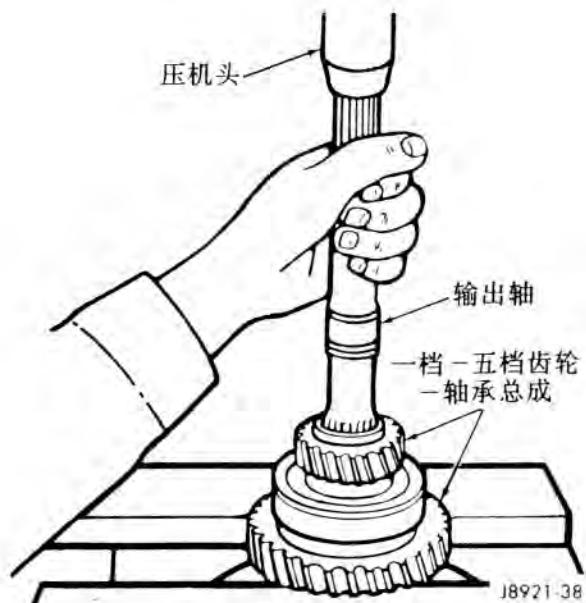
拆卸五档齿轮、一档齿轮、后轴承和轴承内座圈
